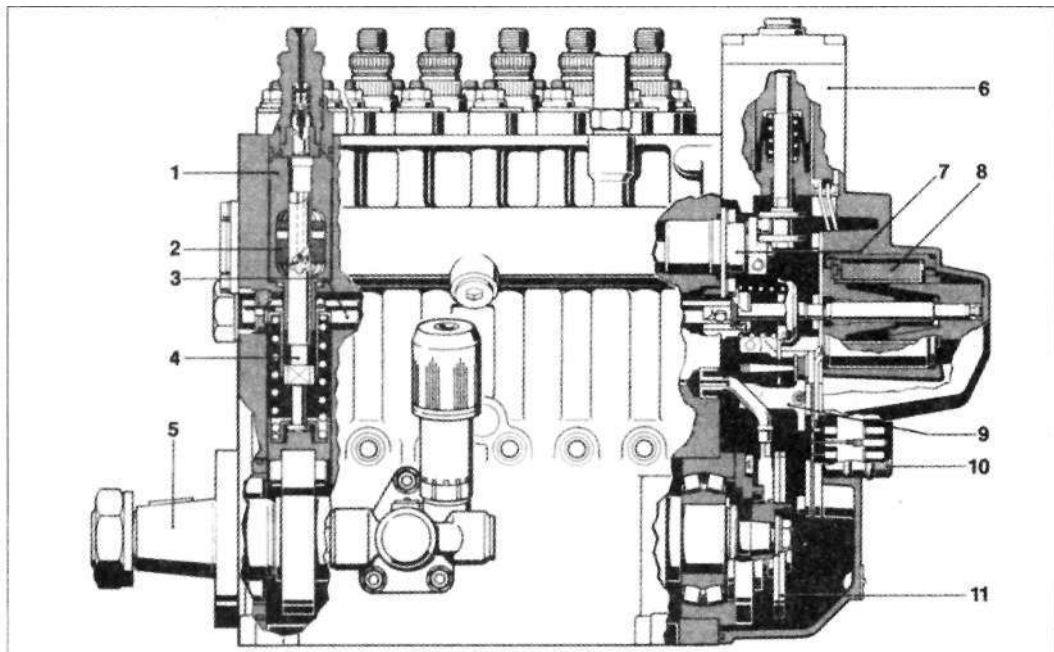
Внешний вид и частичный разрез рядного ТНВД с дополнительной втулкой (источник: Bosch [22]): 1 — гильза плунжера; 2 — дополнительная втулка; 3 — рейка ТНВД; 4 — плунжер; 5 — кулачковый вал; 6 — исполнительный механизм начала подачи; 7 — валик установки дополнительной втулки; 8 — исполнительный механизм изменения хода рейки ТНВД; 9 — датчик хода рейки ТНВД; 10 — итекер соединения с блоком управления; 11 — шайба блокировки начала подачи
